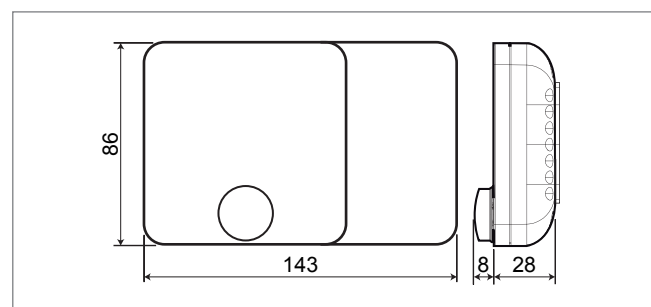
Maßblatt für das Zonen-Bediengerät für Aufputzmontage (Maße in mm)
